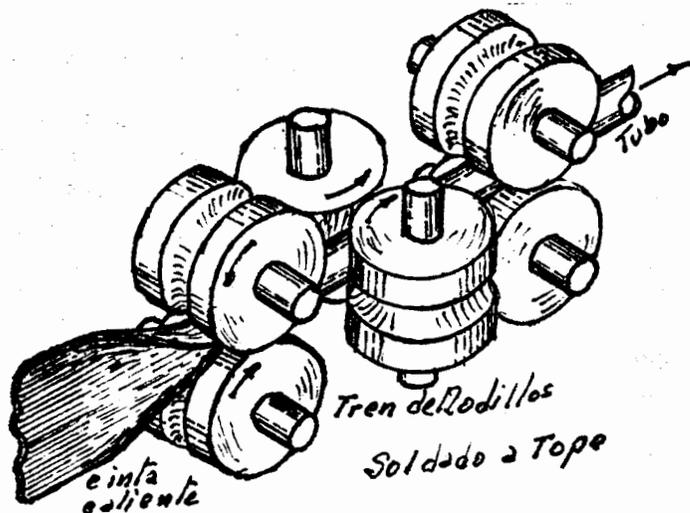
TREN DE RODILLOS PARA FORMADO DE TUBOS SOLDADOS A TOPE.
